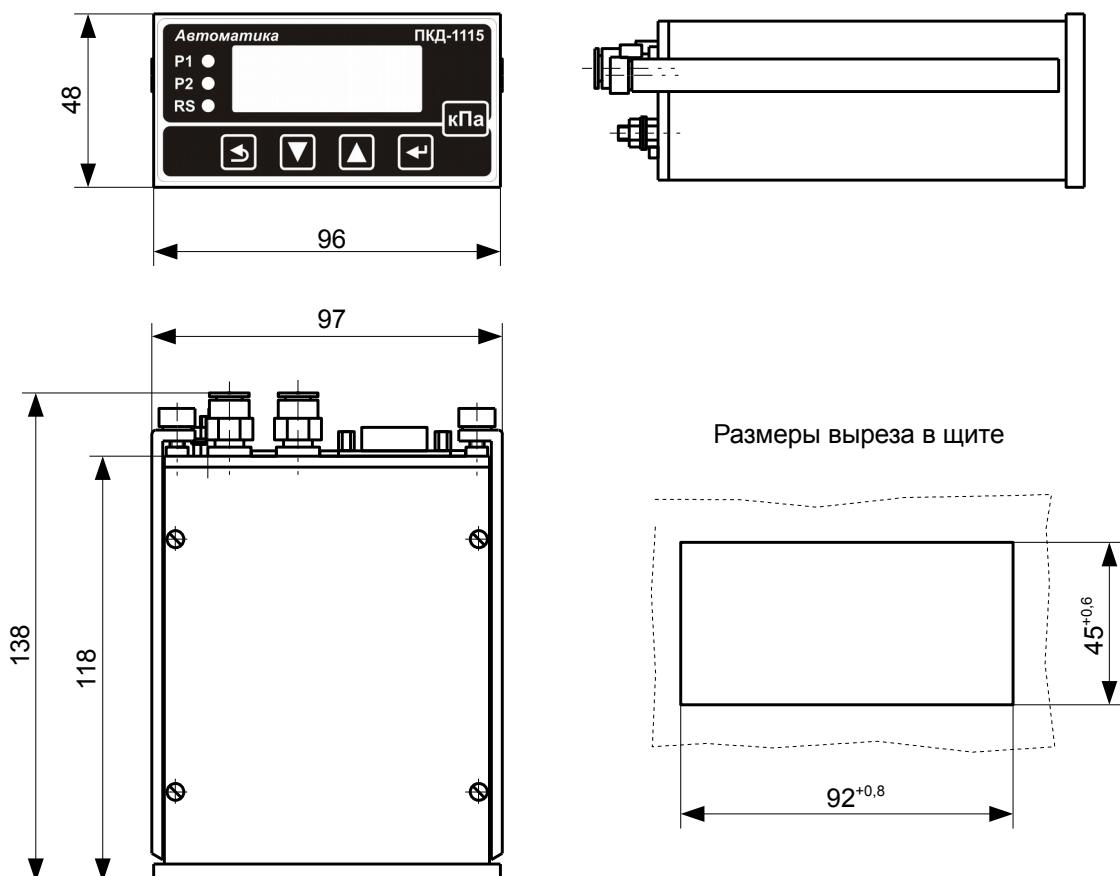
Габаритные размеры ПКД-1115 щитового исполнения
